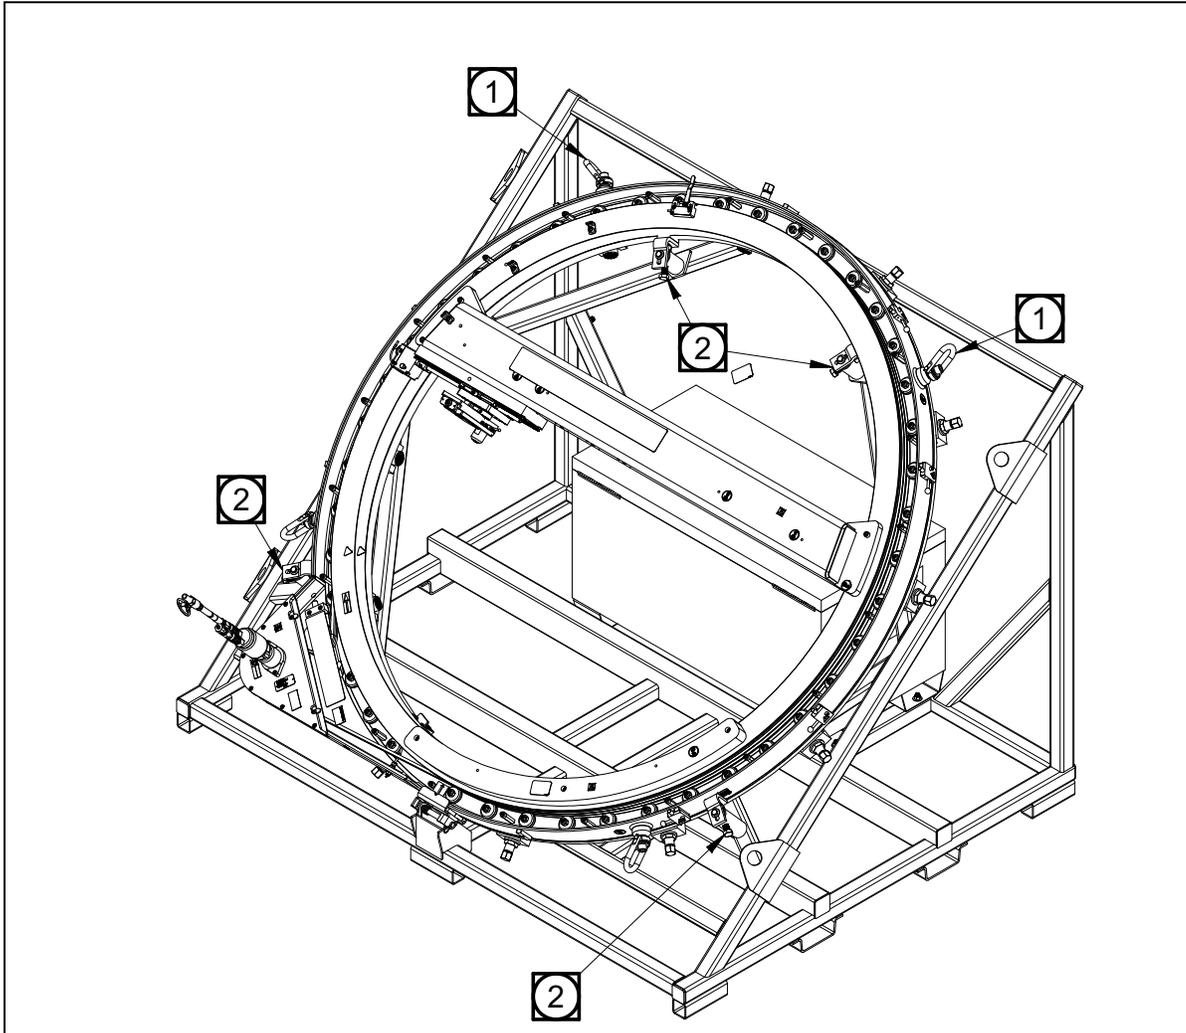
CHÂSSIS DE TRANSPORT INCLINÉ TYPE DE LA MACHINE SPEED FACE (ILLUSTRATION AVEC LA MACHINE ODF80)
